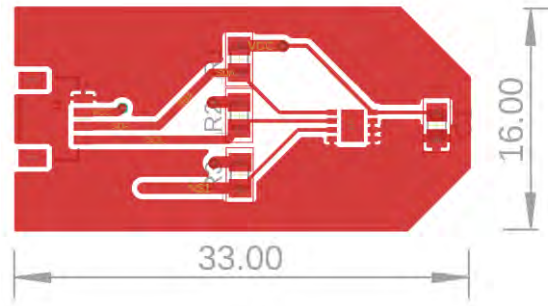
Vista de la superficie de la tarjeta PCB del bloque de temperatura
